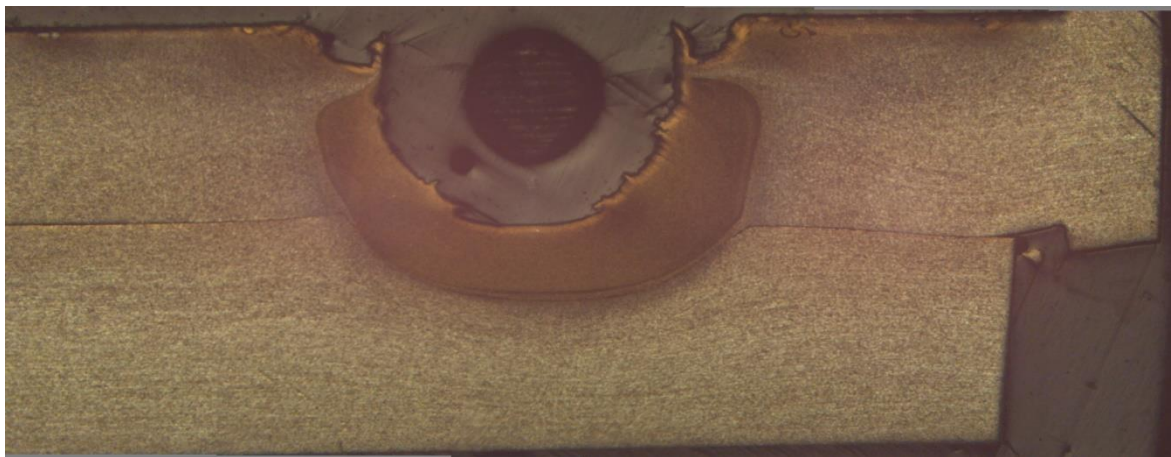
Macrografia do provete soldado W-2.6.
